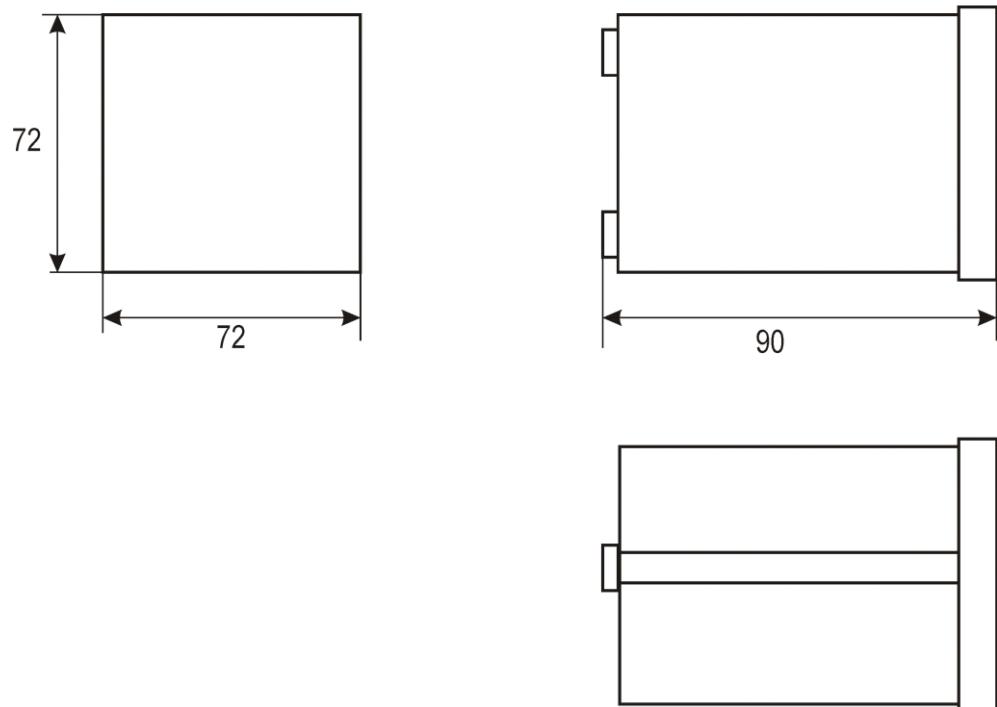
Габаритные размеры ИП для конструктивного исполнения М
